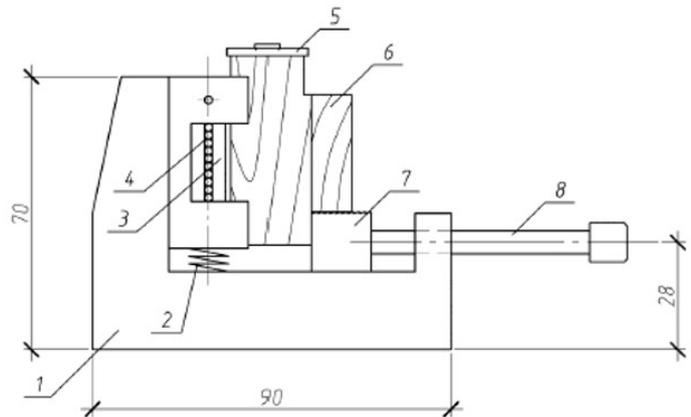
Схема приспособления для определения прочности при скалывании по клеевому слою массивной древесины: 1 - корпус; 2 - пружина; 3 - подвижная планка; 4 - ролики; 5 - нажимная призма с шаровой опорой; 6 - образец; 7 - подвижная опора; 8 - устройство для прижима подвижной опоры
